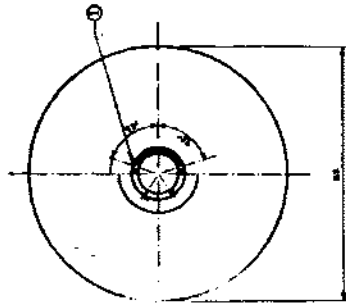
pistón cilíndrico de bronce, dimensiones en mm
